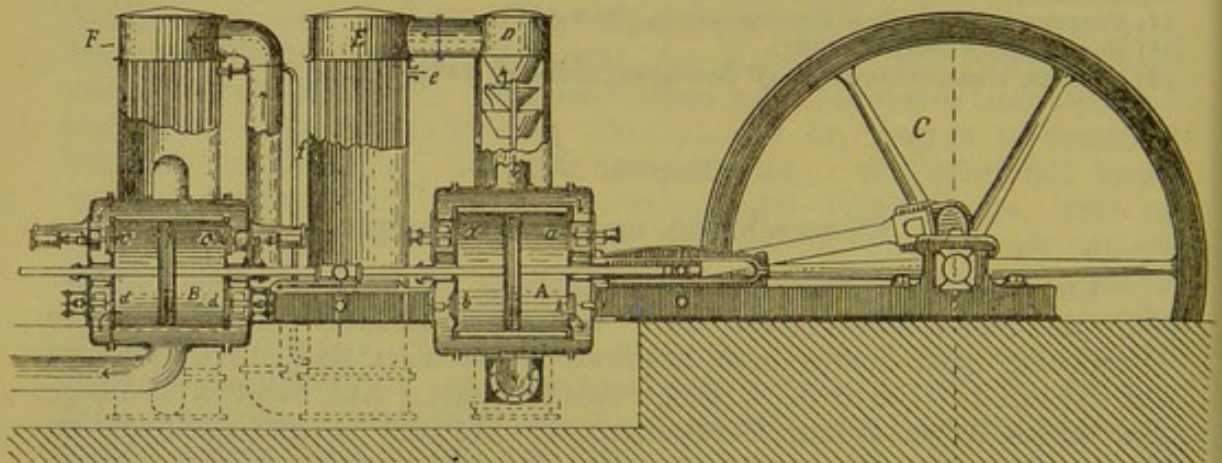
Kühlmaschine. *C* Maschinen für die Bewegung der Kolben, *A* Kompressionszylinder, von einem mit Kühlwasser gefüllten Mantel umgeben, *B* Expansionszylinder, *E* u. *F* Kühlapparate zur Kühlung der durch Kompression erhitzten Luft, *D* Entwässerungszylinder, in dem die aus *A* kommende Luft ihre Feuchtigkeit an den Trichterwänden absetzt. Diese tropft in der Richtung der nach unten zeigenden Pfeile ab, *a* Saugventile des Kompressionszylinders, *b* Druckventile des Kompressionszylinders, *c* Einlassventile für die abgekühlte komprimierte Luft, *d* Auslassventile für die abgekühlte expandierte Luft, *f* Zufuhrrohr für Kühlwasser, *e* Abflußrohr für Kühlwasser. Nach Schwarz⁶⁰.
